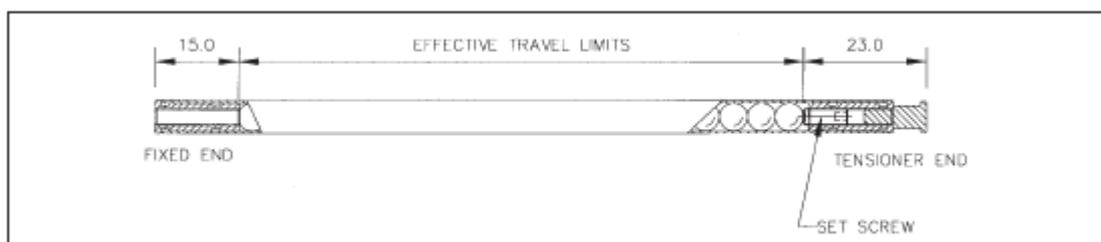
Installazione Scale con Corsa Utile oltre 2,5mt e dettaglio dei supporti Intermedi
